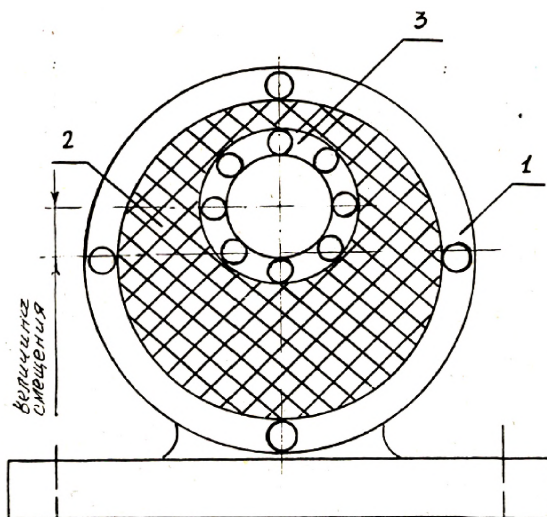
Подшипниковая опора с упругой подушкой для пильного цилиндра джина
